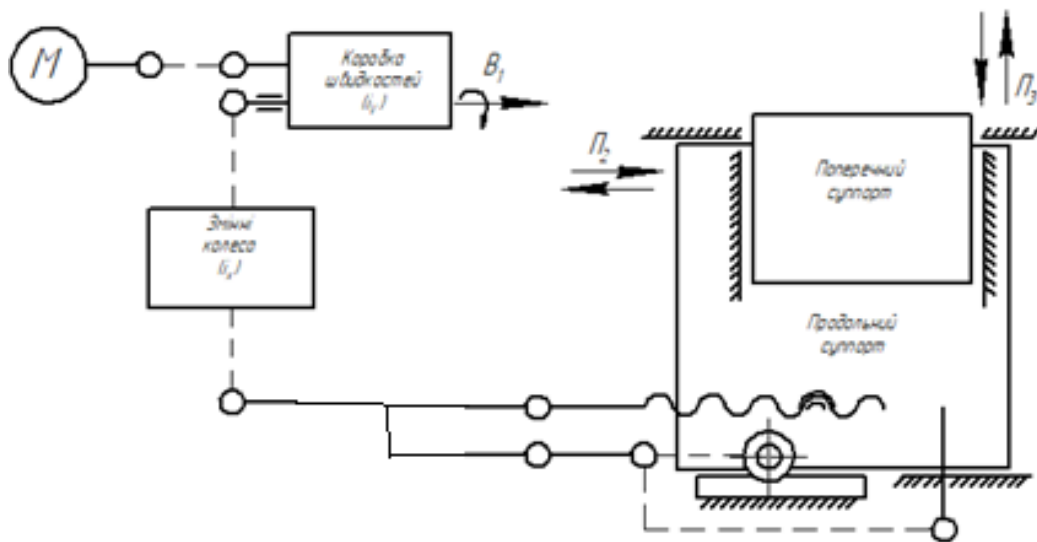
Принципова схема кінематичних зв'язків токарно-гвинторізного верстата
